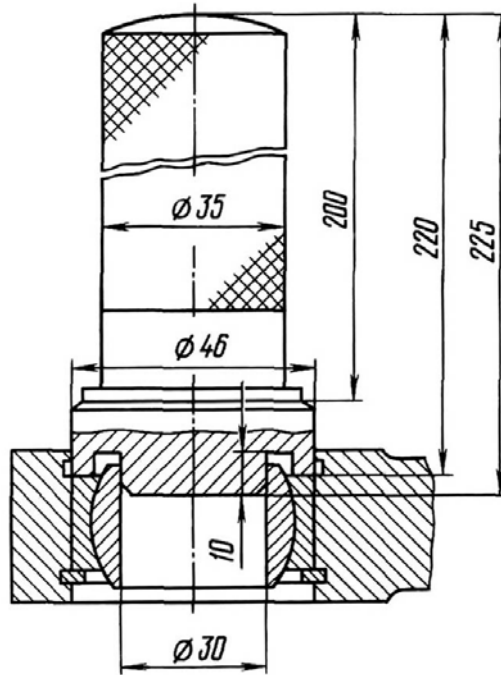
Оправка для запрессовки и выпрессовки шарнирного подшипника
